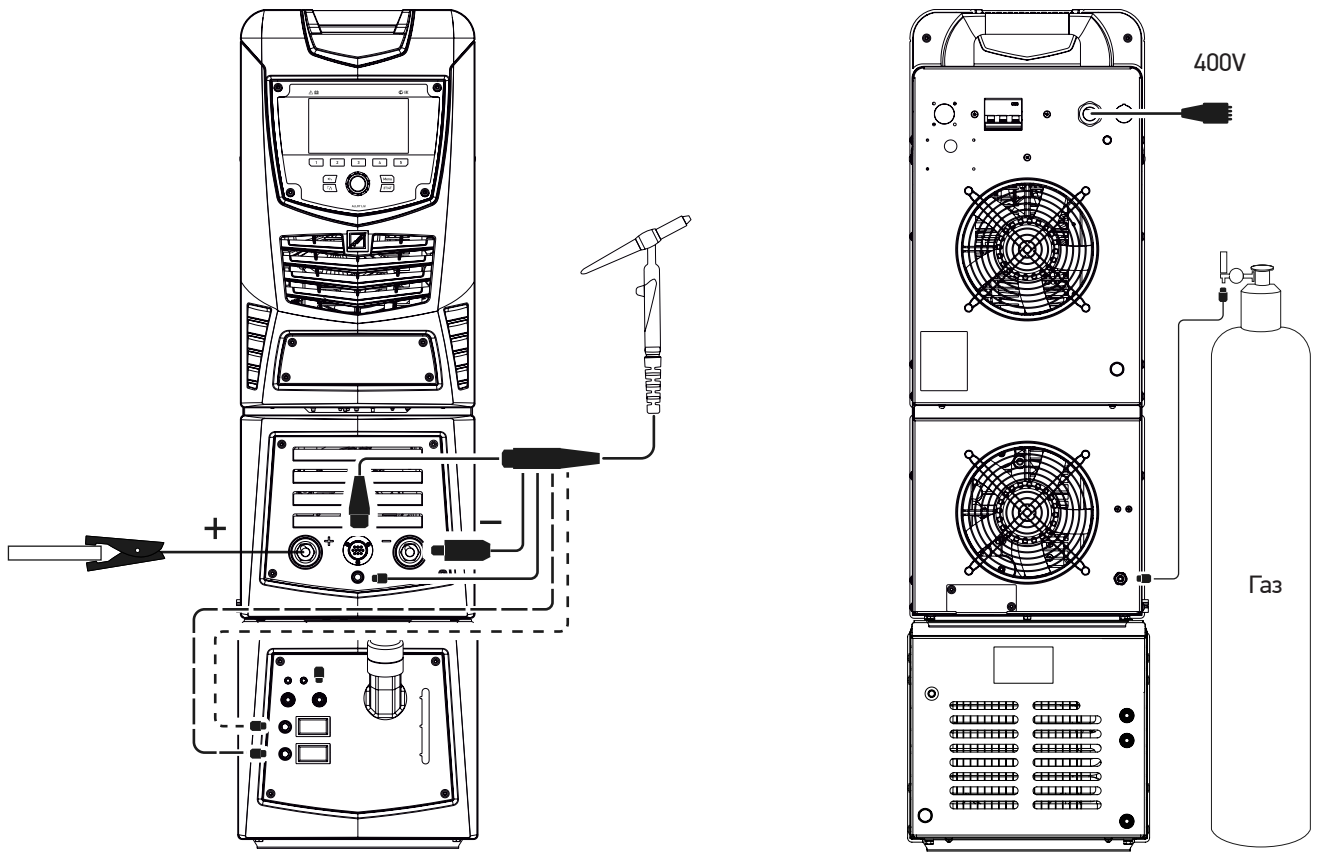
Схема соединений комплекта сварочного оборудования TIG
